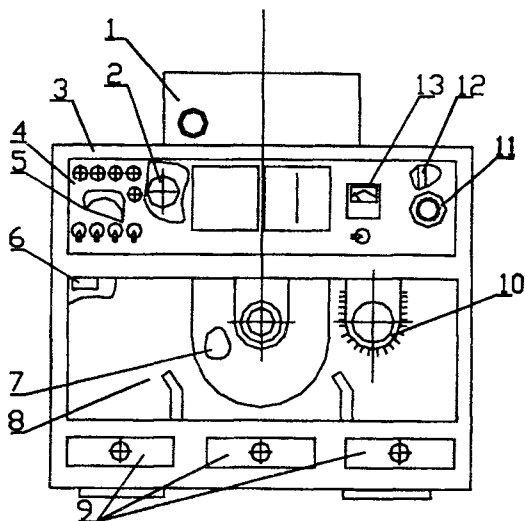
Сепаратор семян диэлектрический лабораторный СДЛ-1 (общий вид): 1 – бункер; 2 – электродвигатель; 3 – корпус; 4 – панель управления; 5 – мотор-редуктор; 6 – конечный выключатель; 7 – барабан; 8 – защитные стекла; 9 – кассеты; 10 – щетка; 11 – автотрансформатор; 12 – высоковольтный трансформатор; 13 – вольтметр
